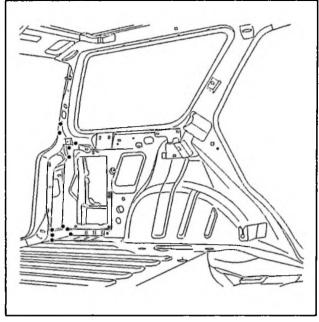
P044C Souder par points "bouchon" MAG. Meuler les points de soudure MAG.
